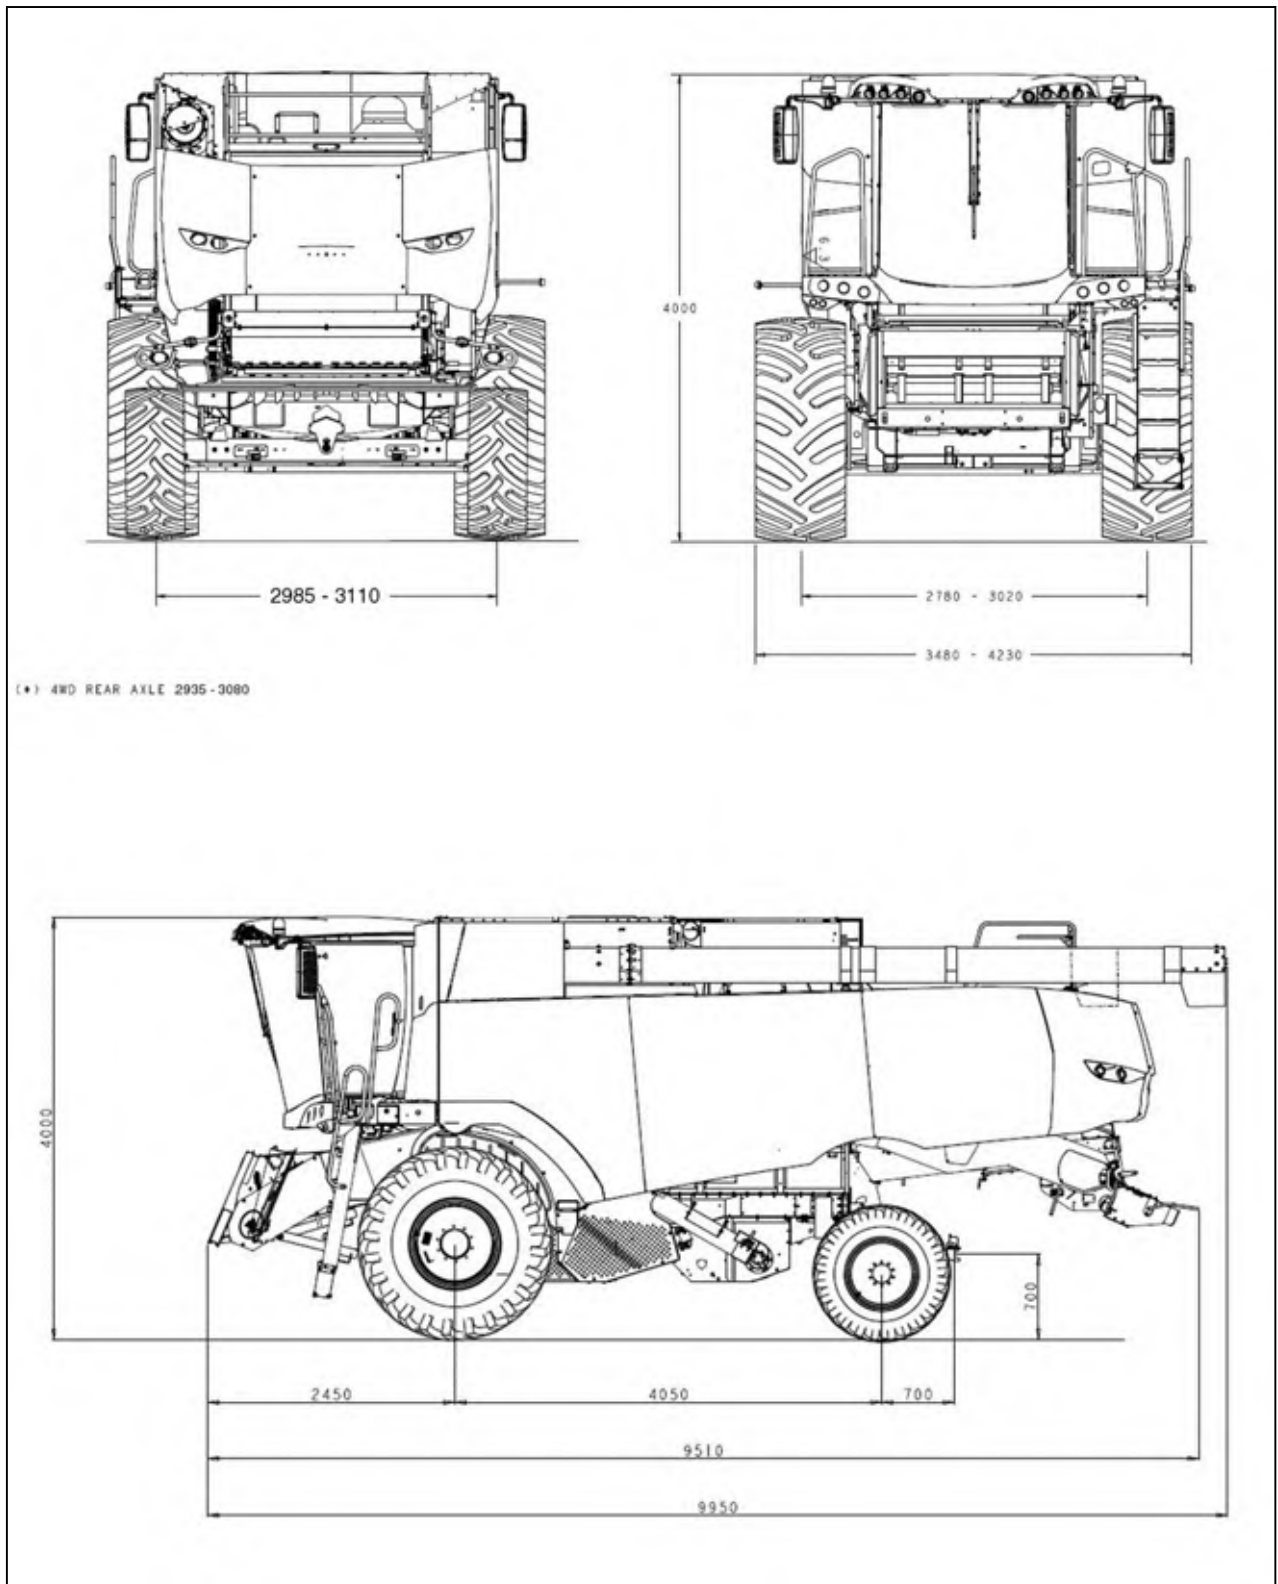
Dimensioner for maskine med dæk; front, bag, side
